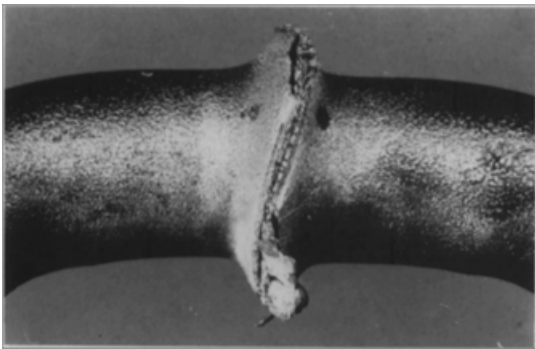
Stauchgrat einer Preßstumpfschweißung an einem Kettenglied;
